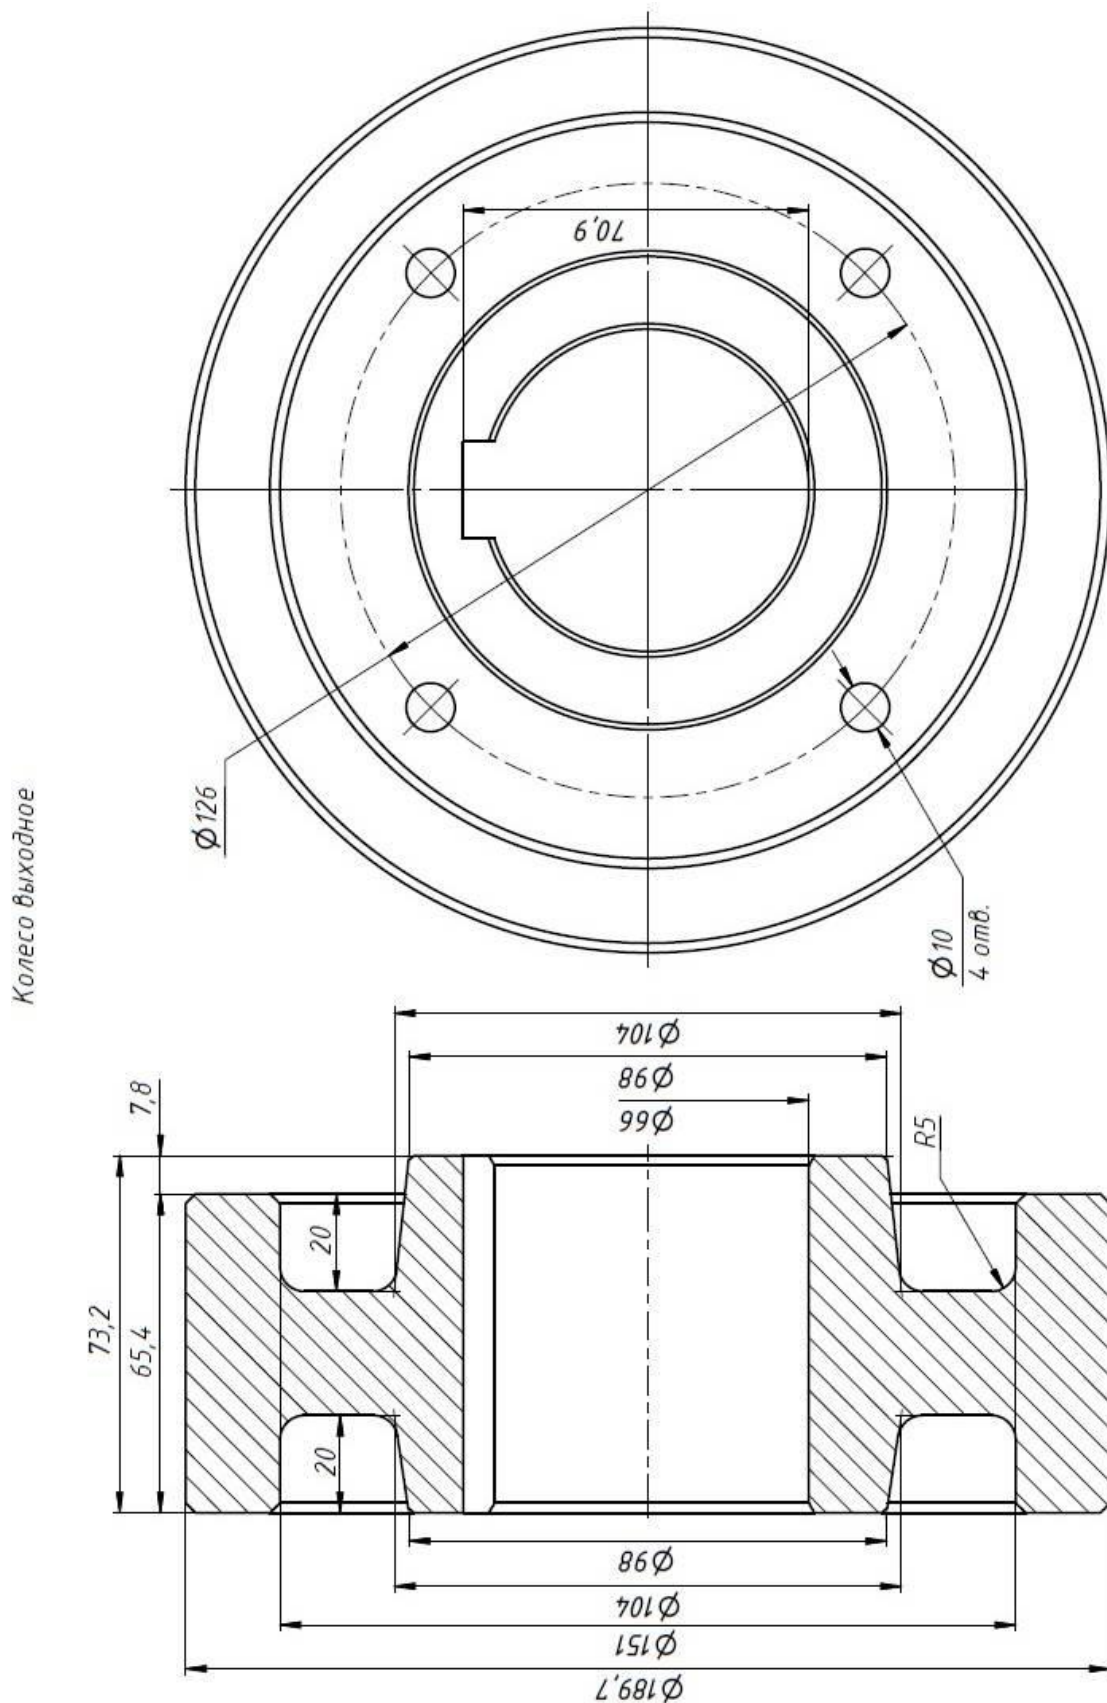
Чертеж колеса выходного редуктора с эвольвентным зубчатым зацеплением
